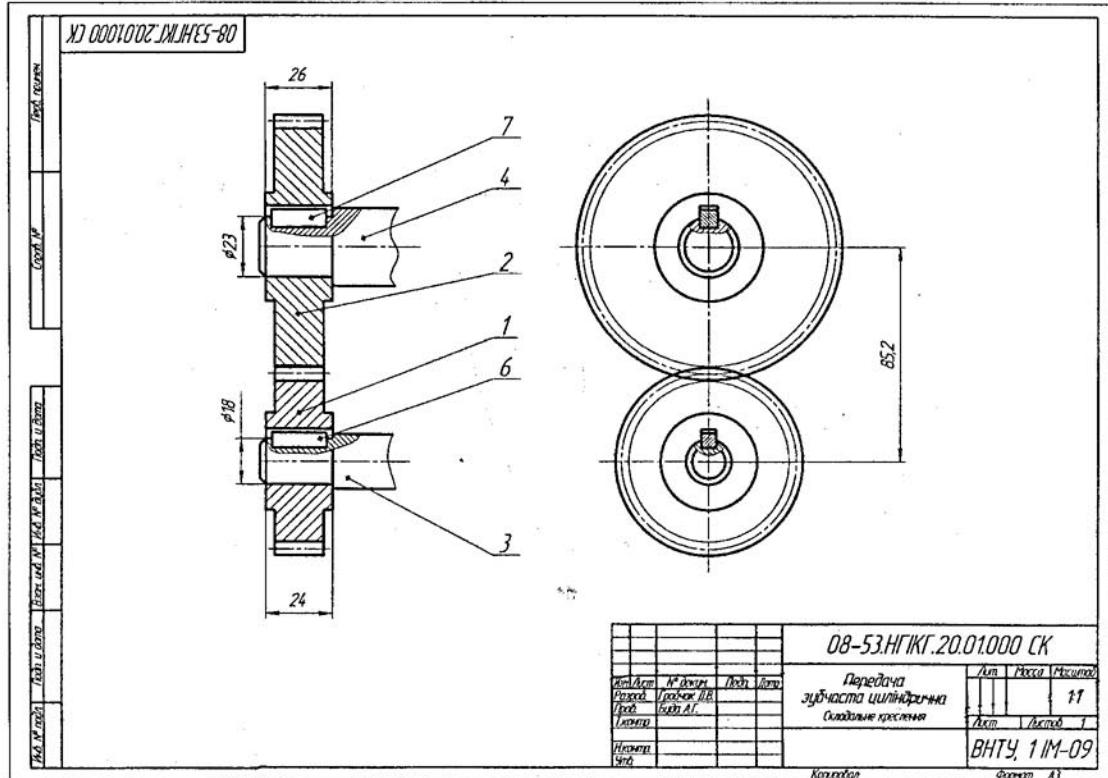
Зразок виконання циліндричної зубчастої передачі
